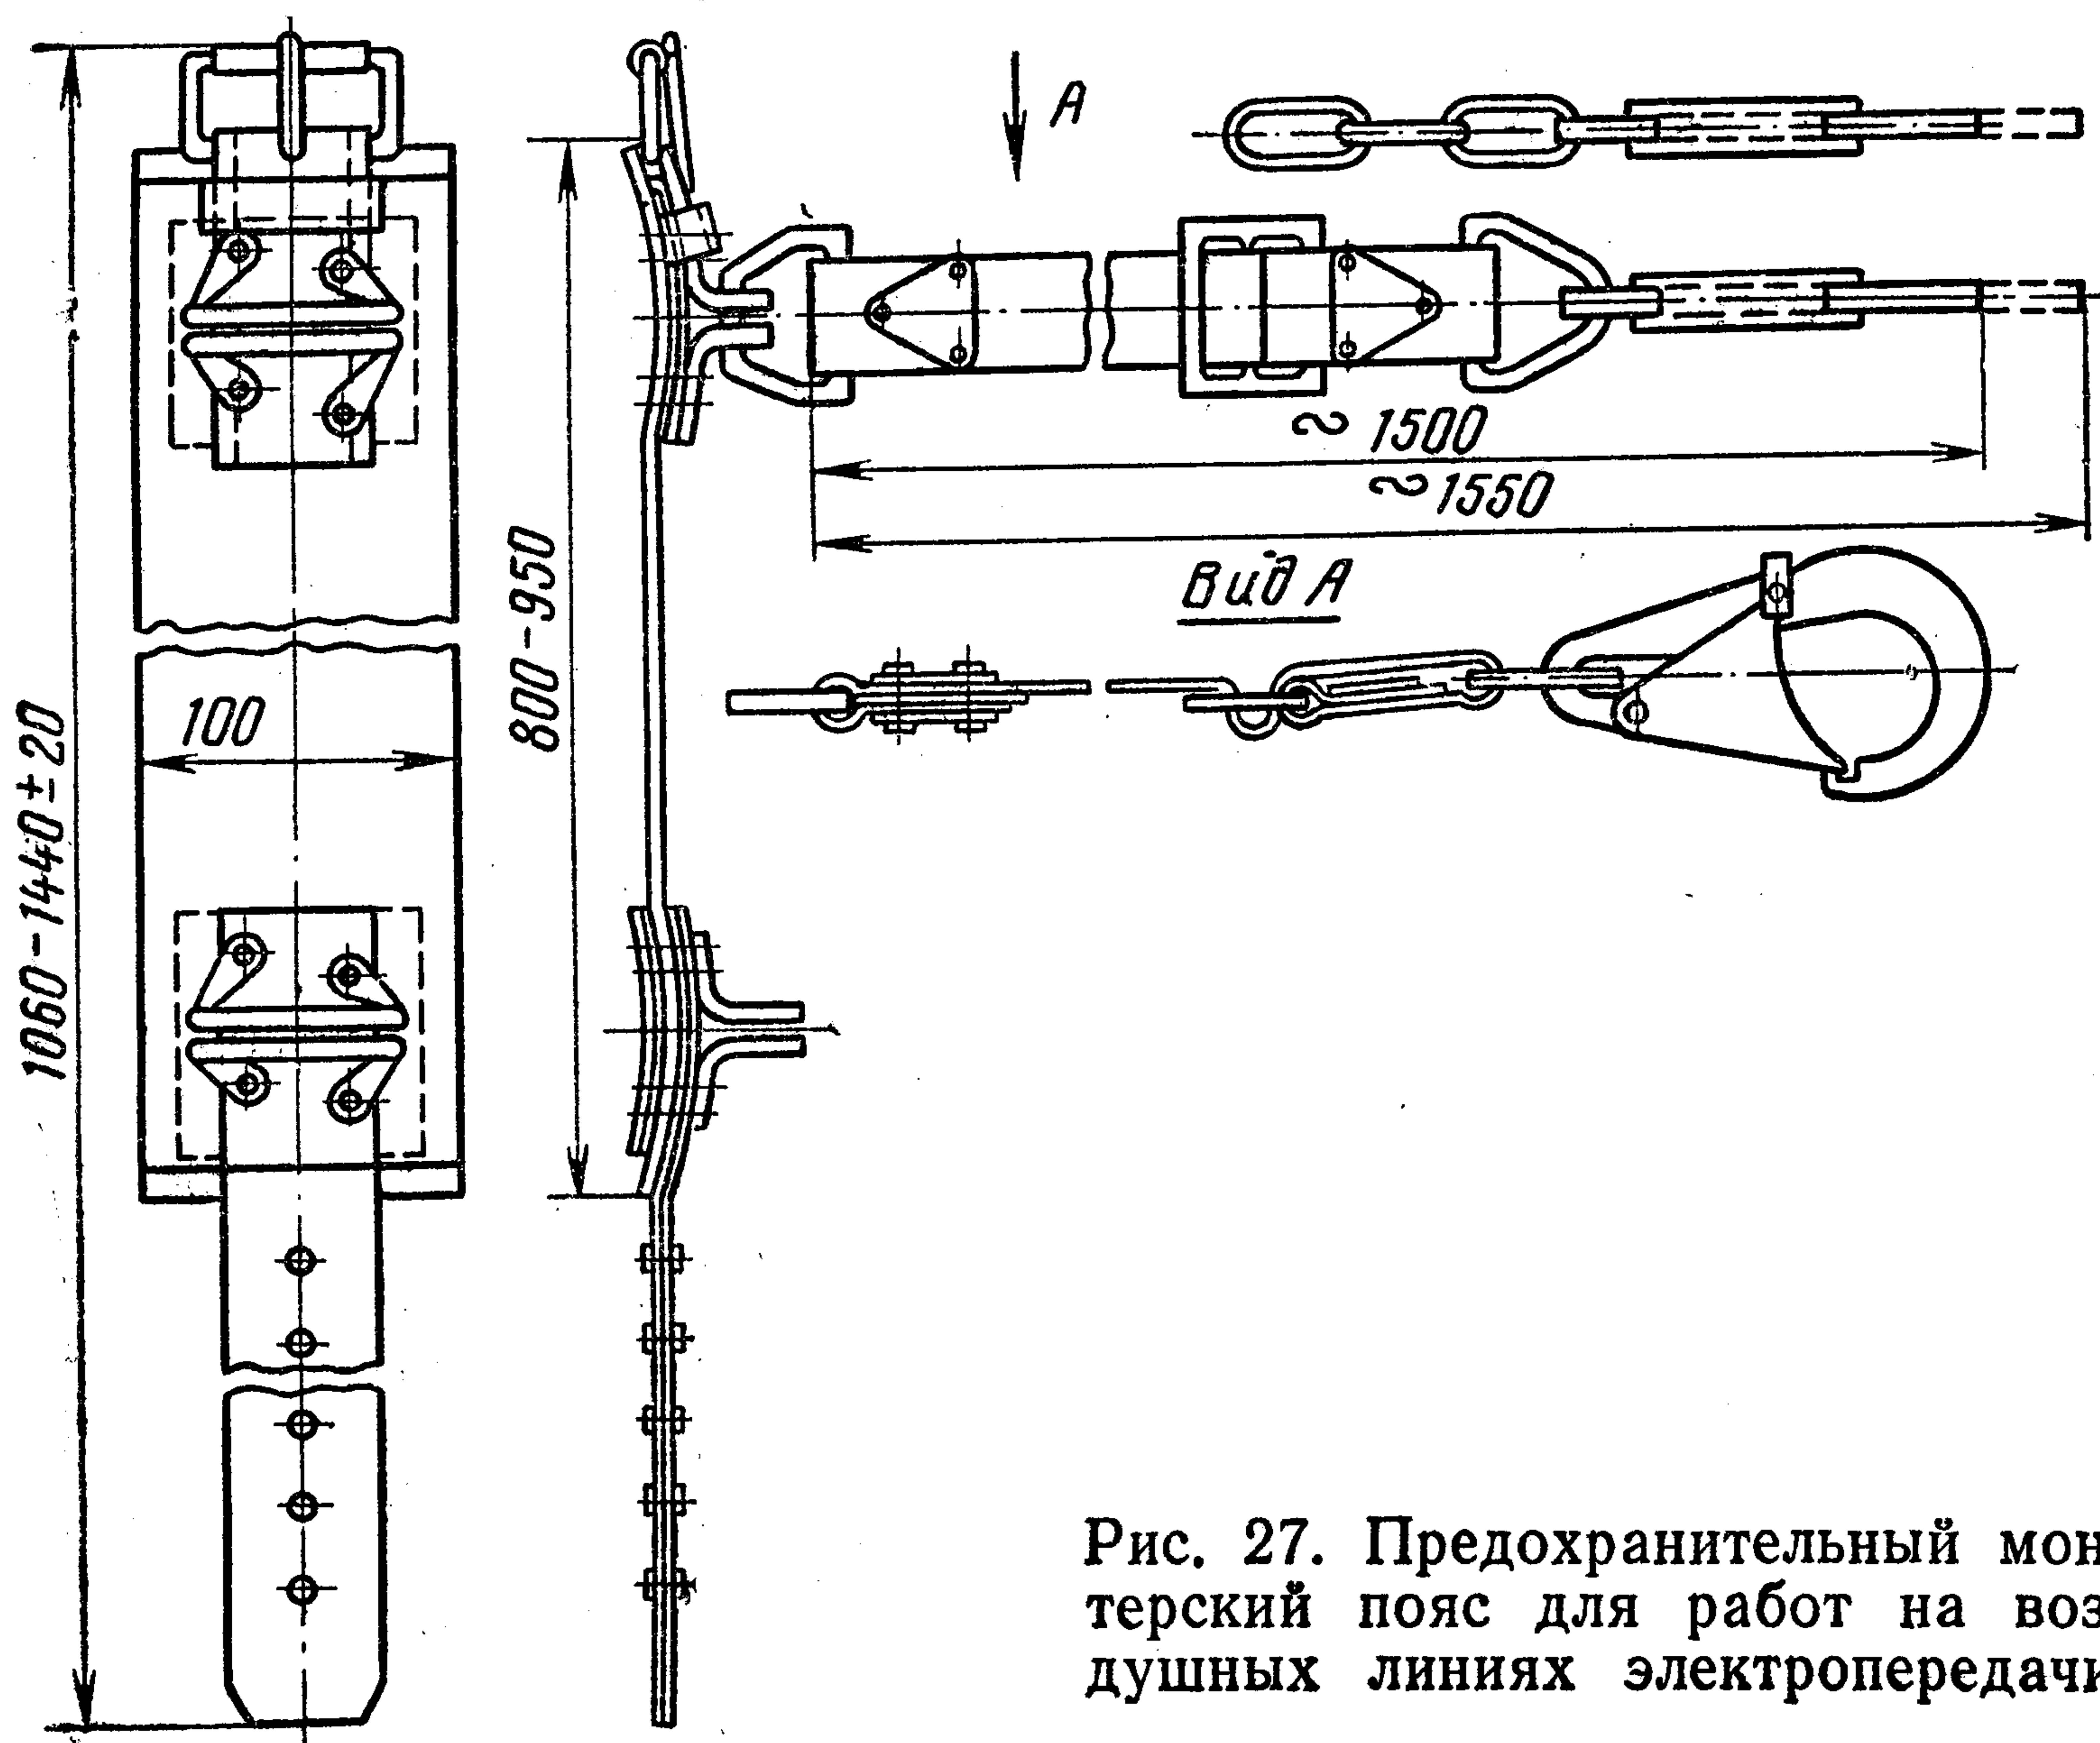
Предохранительный монтажный пояс для работ на воздушных линиях электропередачи.
